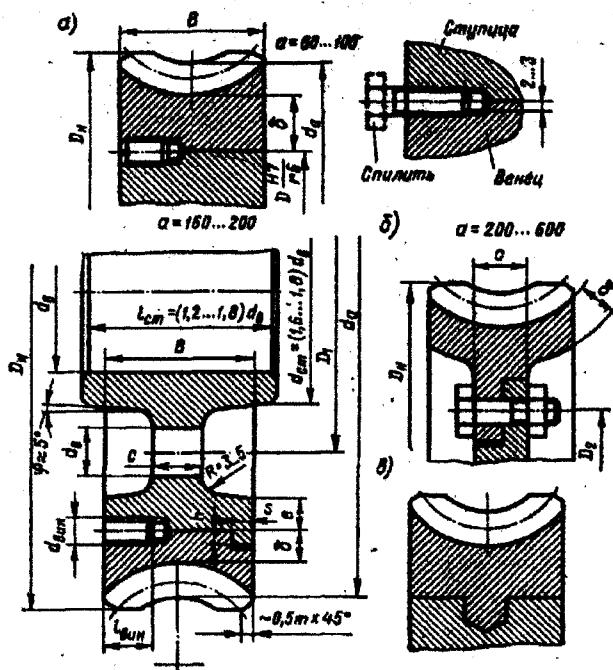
Способы соединения зубчатого венца со ступицей колеса
